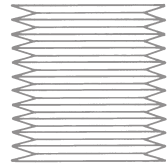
Faltenbalg mit geschweißten Blättern
